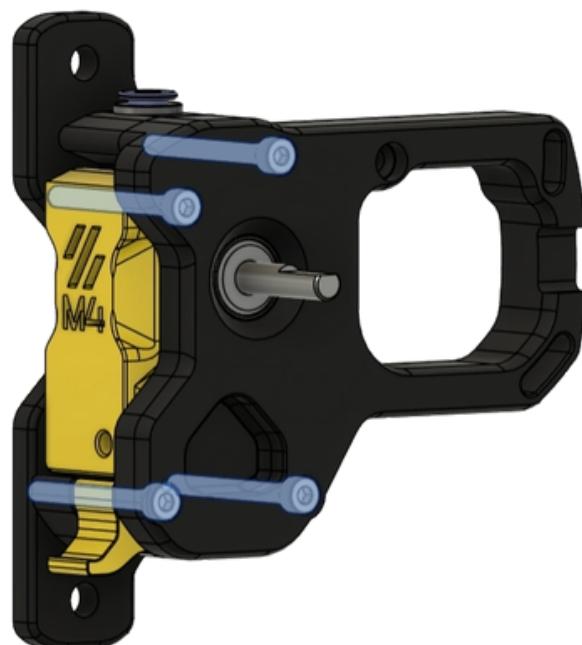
Pieza [a]_guidler posicionada y ajustada.
